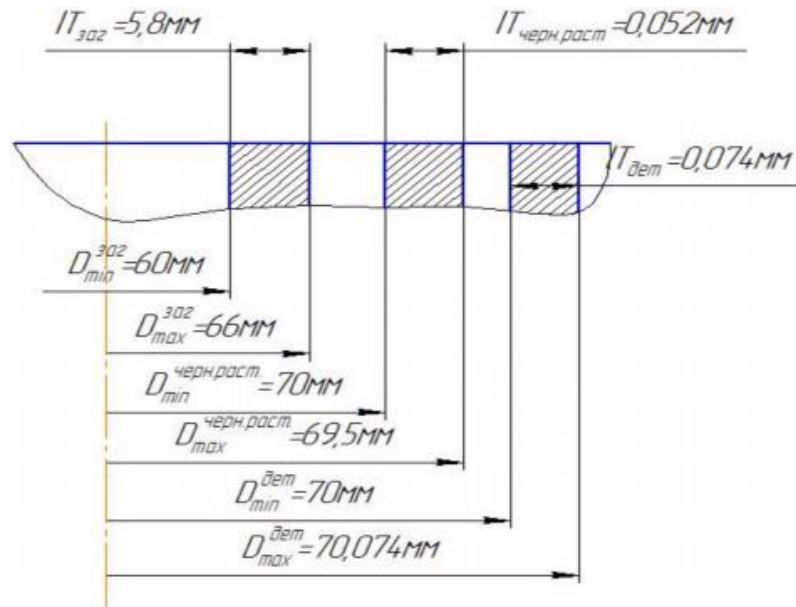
Схема розташування припусків, допусків та між операційних розмірів для отвору $\varnothing 70H9$
